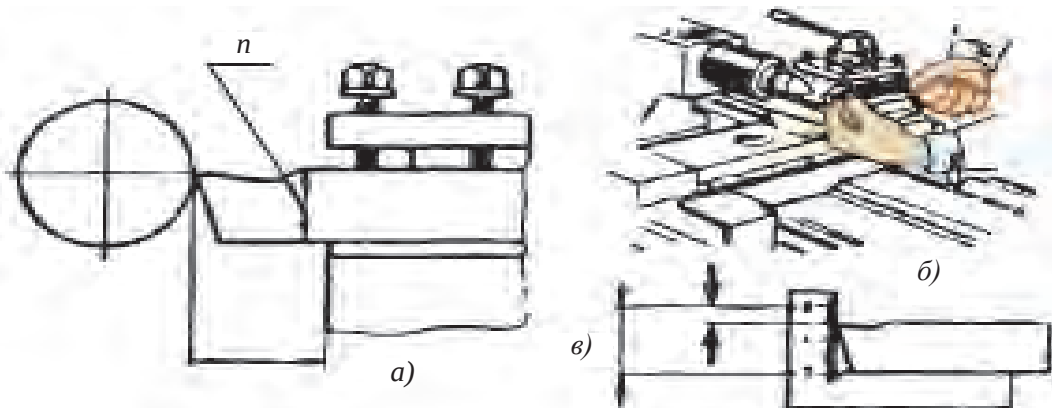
а – резец и держатель резца; б – проверка высоты резца; в – угловой шаблон.
